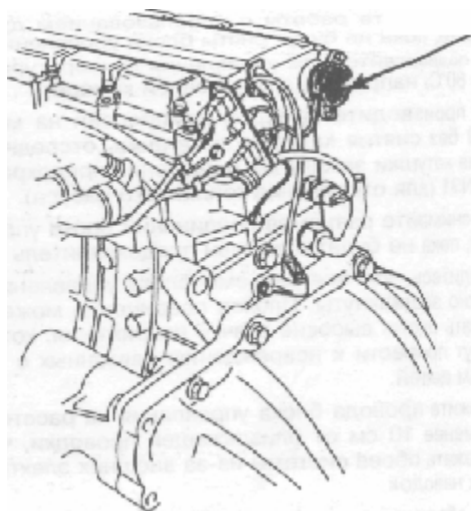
Датчик распределительного вала расположен в задней части головки блока цилиндров и приводится выступом распределительного вала — Volvo 960
